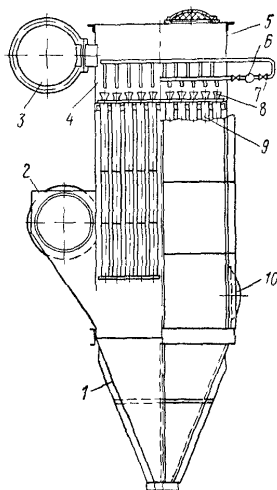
Металлокерамический фильтр: 1 – бункер; 2 – коллектор входной; 3 – то же, выходной; 4 – сопла; 5 – корпус; 6 – коллектор компрессионного воздуха; 7 – электромагнитный клапан; 8 – насадки; 9 – фильтрующие элементы; 10 – люк.
